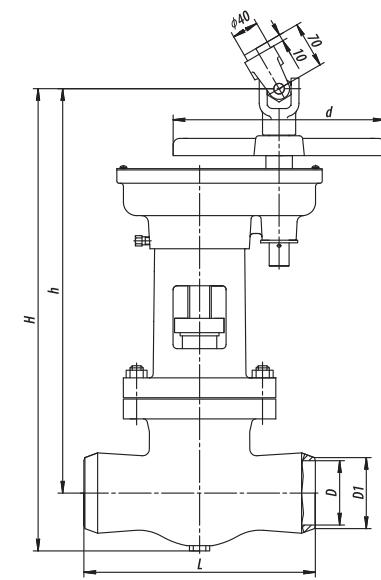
Задвижка DN80-100 с цилиндрическим редуктором
